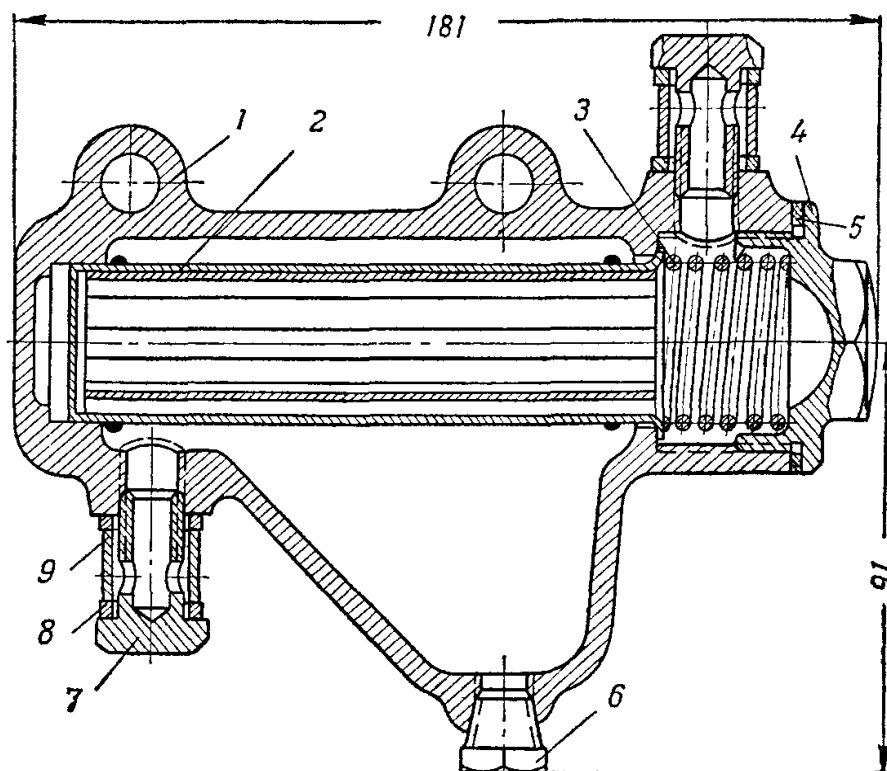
Топливный фильтр грубой очистки дизеля:
